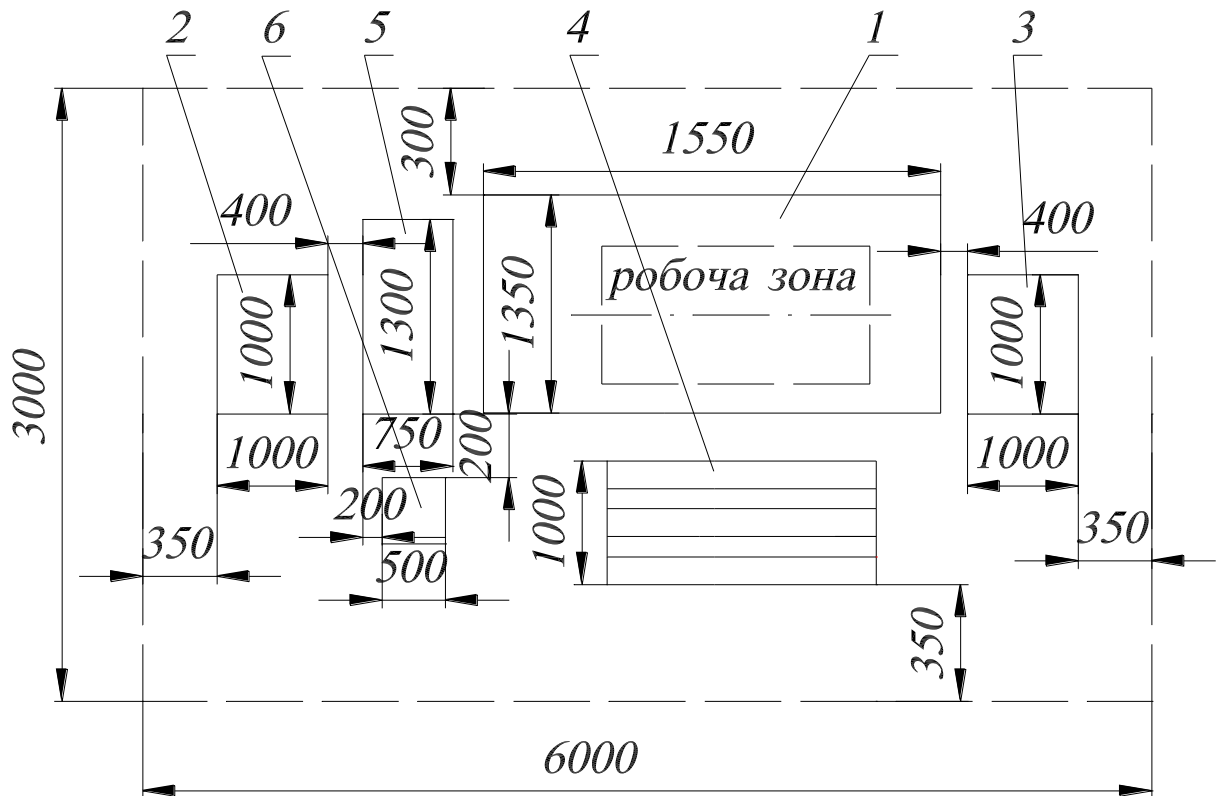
Схема робочого місця на верстаті (1 – верстат; 2– тара для заготовок; 3– тара для деталей; 4– решітка під ноги; 5 – електрошафа і система ЧПК; 6 – лоток для інструменту).
